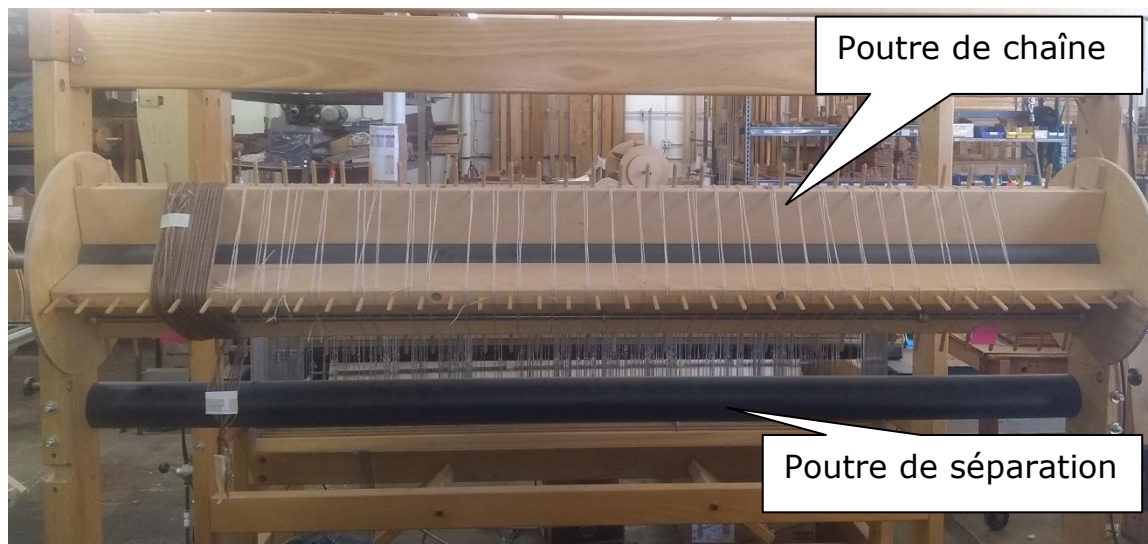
Poutre de chaîne et poutre de séparation sur métier à tisser en bois
